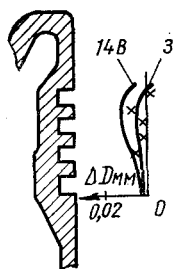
Деформация поршня двигателя Д100 в зоне компрессионных колец
